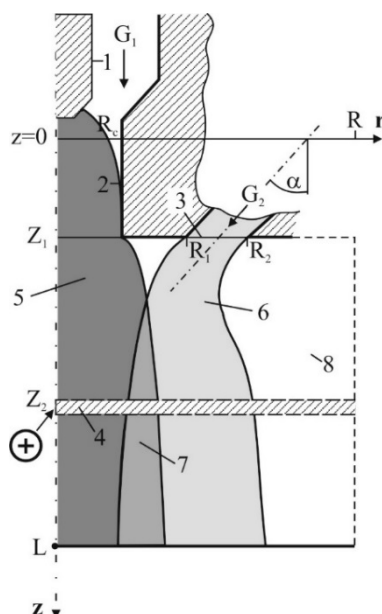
Схема процесса плазменно-дугового проволоочного напыления: 1 – катод; 2 – сопло; 3 – канал подачи обдувающего газа; 4 – проволока-анод; 5 – дуговая плазма; 6 – обдувающий газ; 7 – область смешения; 8 – внешняя газовая среда
